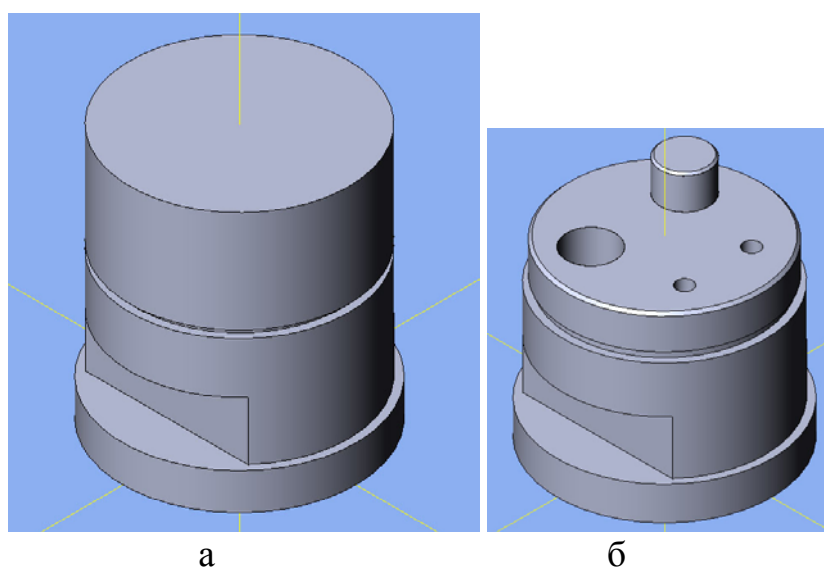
3D-модель заготовки (а) и 3D-модель (б) детали “цилиндр”
